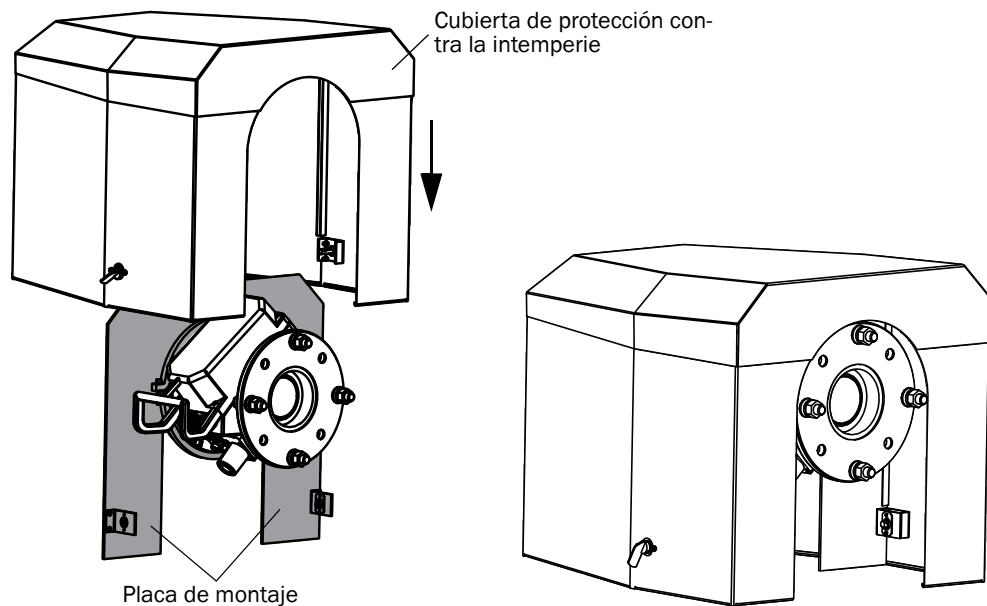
Montaje de la cubierta en el adaptador de aire de purga
